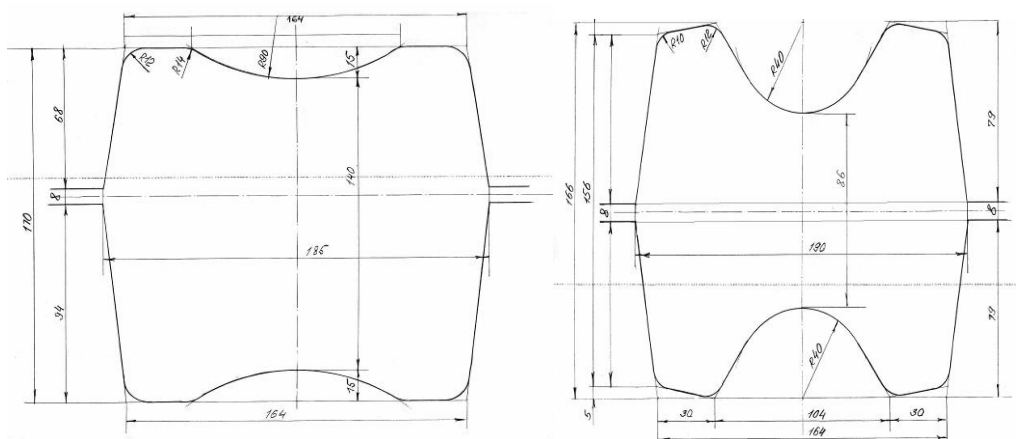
Калибровка обжимной клетки стана 620 ОАО «КМЗ им. Куйбышева»
